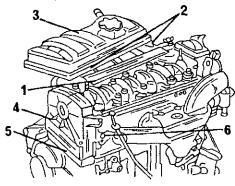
Установка крышки головки цилиндров. Расшифровка цифровых обозначений приводится в
